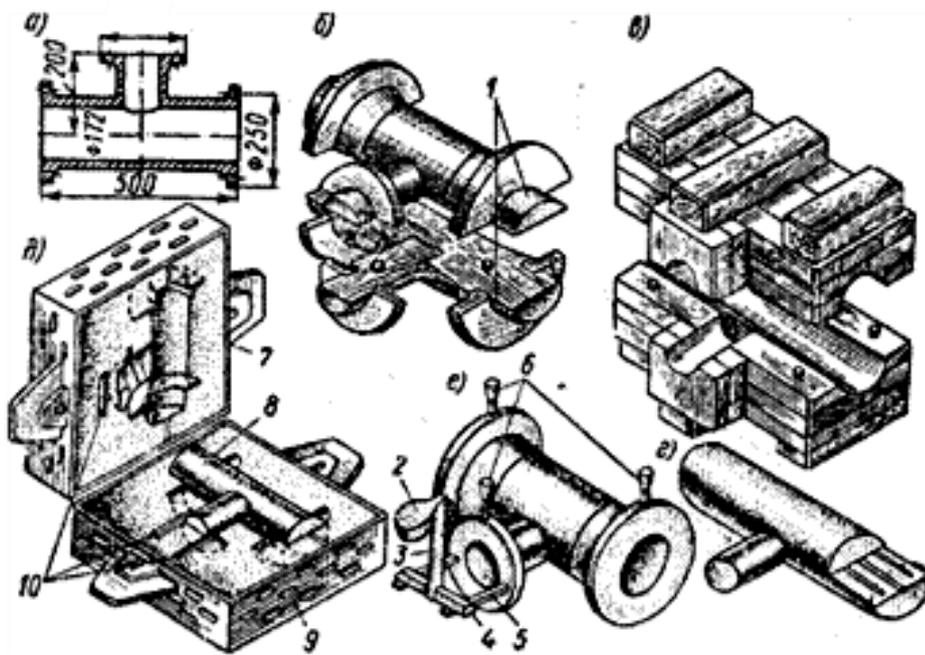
Схема технологического процесса изготовления отливка тройника.
